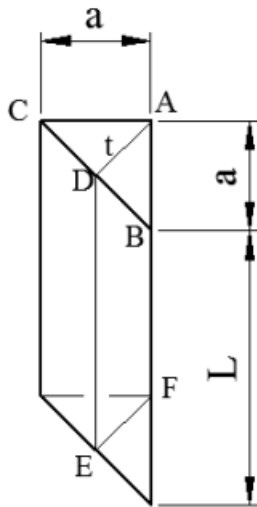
Soldadura de filete (Ringegni, 2013).
